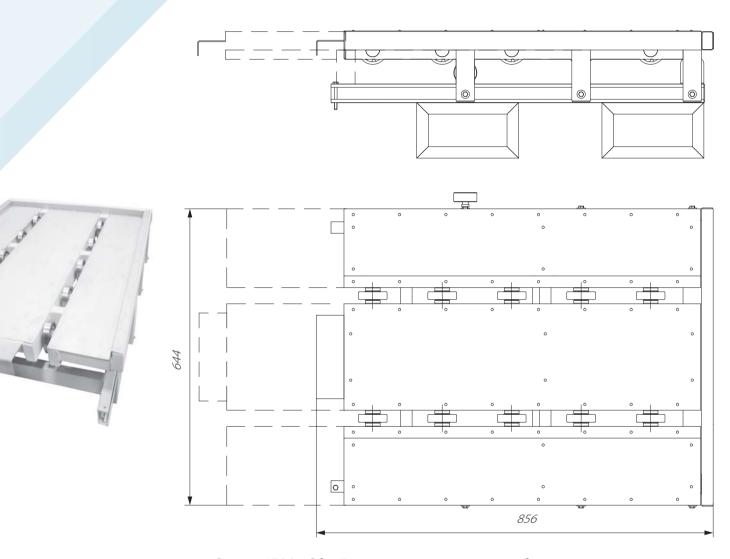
Общий вид перегрузочного приспособления.
